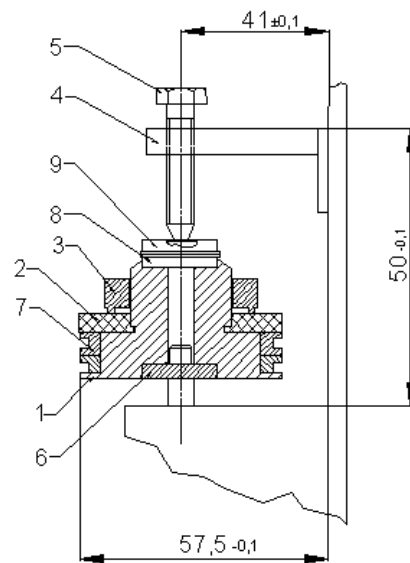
Конструкция устройства для лазерной сварки кольцевых швов корпусов датчиков на установке «Квант-15»: 1-корпус; 2- шайба; 3- гайка; 4- кронштейн; 5- болт; 6- пружина; 7- кольцо; 8- крышка; 9- крышка; 10- привод (условно не показан)
